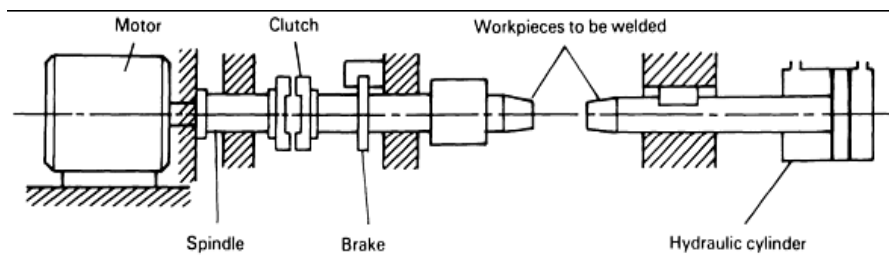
Proses Kerja *Friction Rotary Welding
